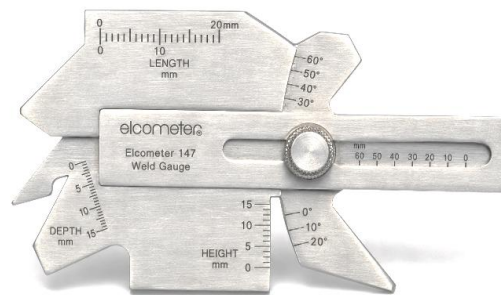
Універсальний зварювальний шаблон Elcometer 147 Weld Gauge [22]
